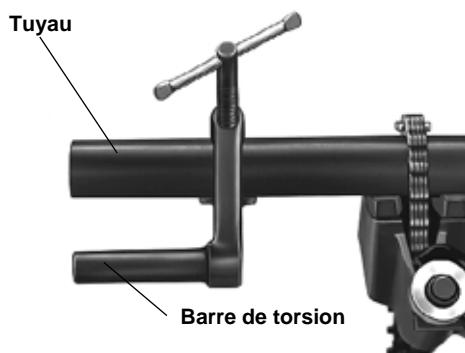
Alignement de la barre de torsion du support de tube n° 601 sur l'extrémité du tuyau
